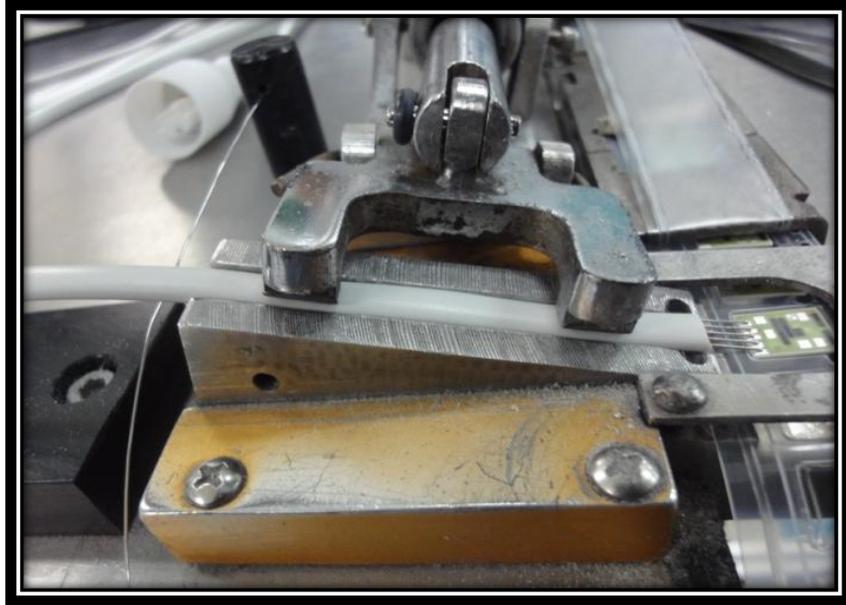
Fixture de soldadura para posicionar el cable.²¹
